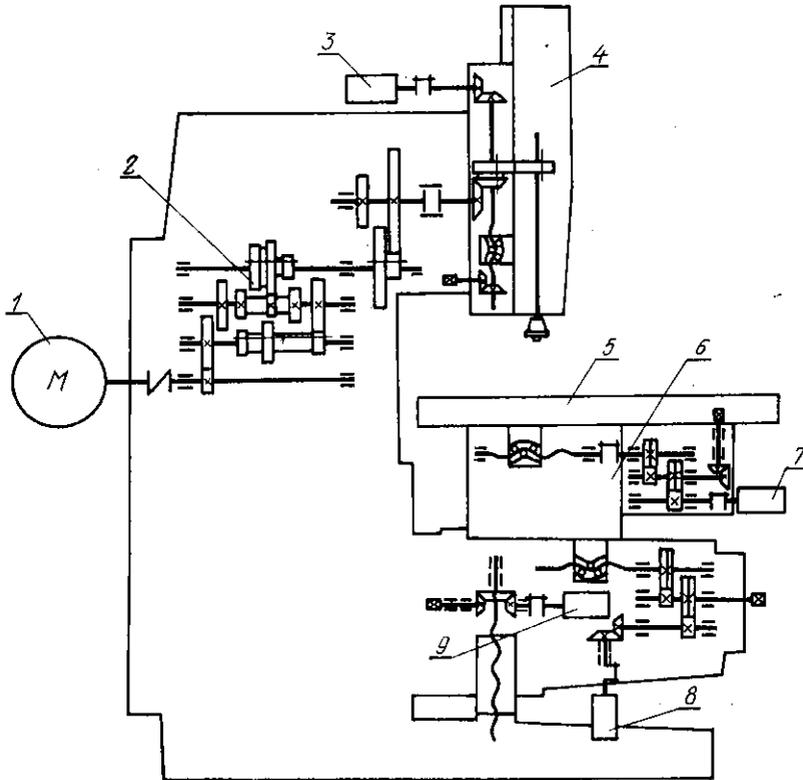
Кинематическая схема вертикально-фрезерного станка 6Р13ФЗ
